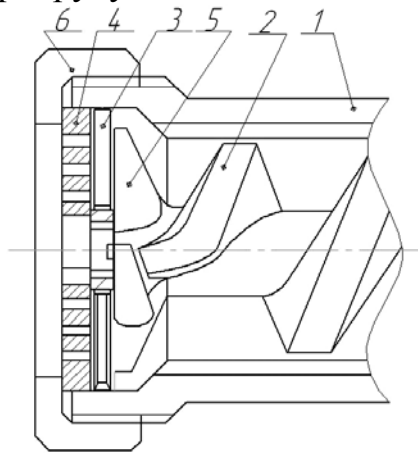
Різальний вузол: 1 - робочий циліндр; 2 - шнек; 3 - ніж-; 4 - ґратка; 5 - виступ; 6 - затяжна гайка
